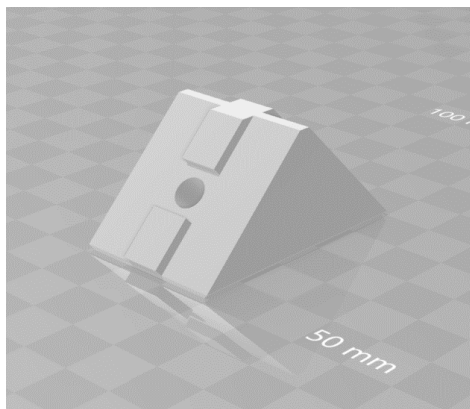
Uchycení motoru spodní pravé Autor: David Trcka
